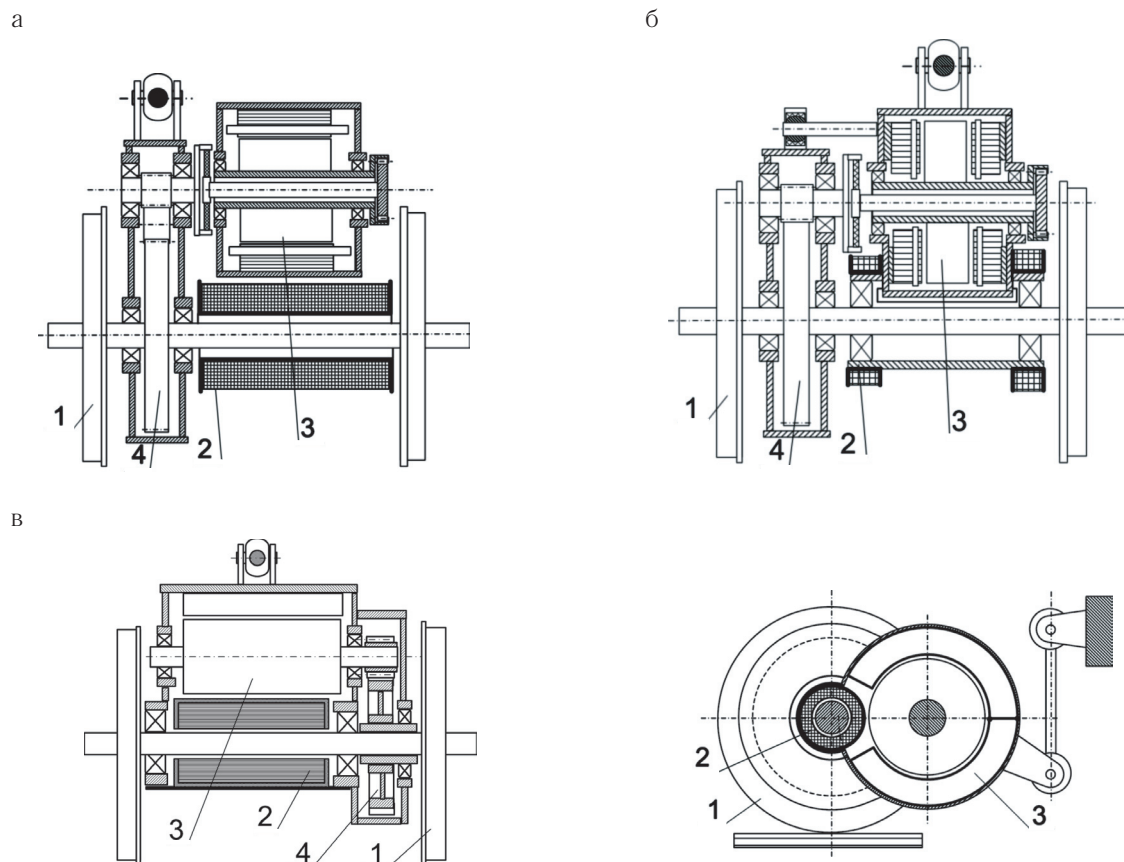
Варианты размещения обмоток индуктора при индивидуальном приводе: а – опорно-рамный привод с осевым редуктором и промежуточным колесом; б – привод с тяговым электродвигателем с осевым магнитным потоком; в – привод с дугогасительным двигателем; 1 – колесная пара; 2 – обмотка индуктора; 3 – тяговый электродвигатель; 4 – редуктор (тяговая передача).
